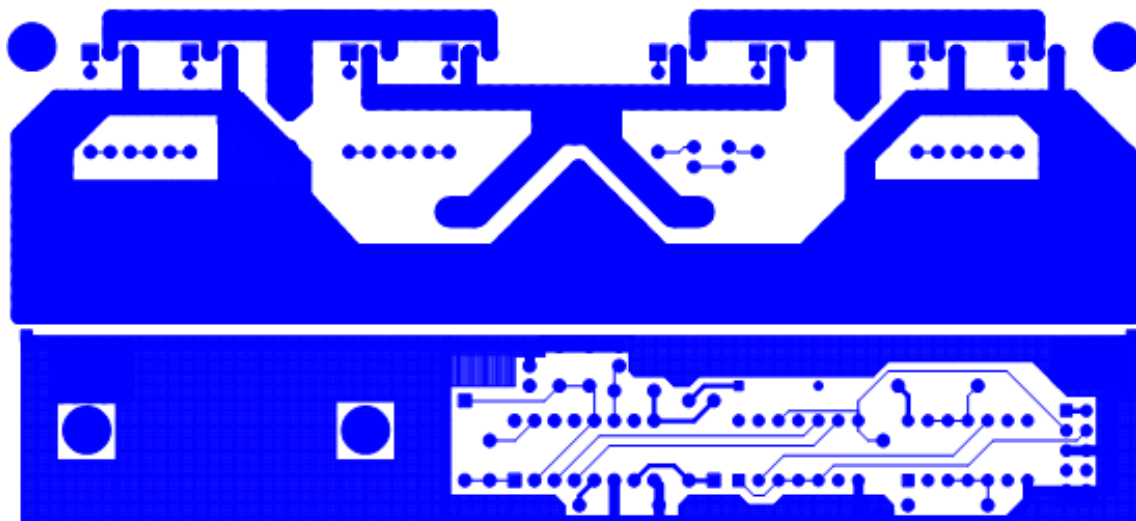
Placa del módulo de potencia Layout final. Capa BOTTOM
